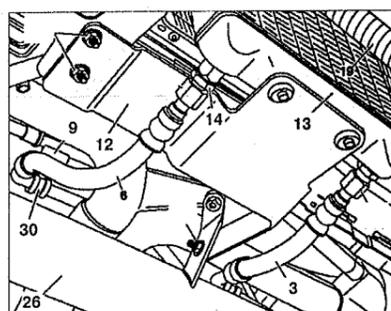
Сливная 6 и нагнетающая 3 трубки автоматической коробки передач.
